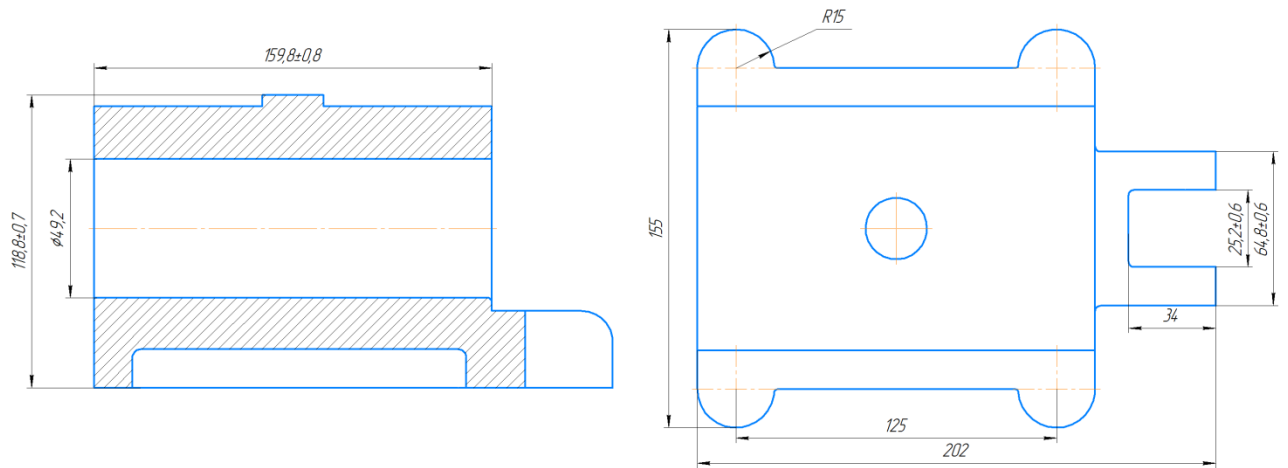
Ескіз заготовки виливок у піщані форми з машинною формовкою 8-го класу точності розмірів та мас, 2-го ряду припусків
